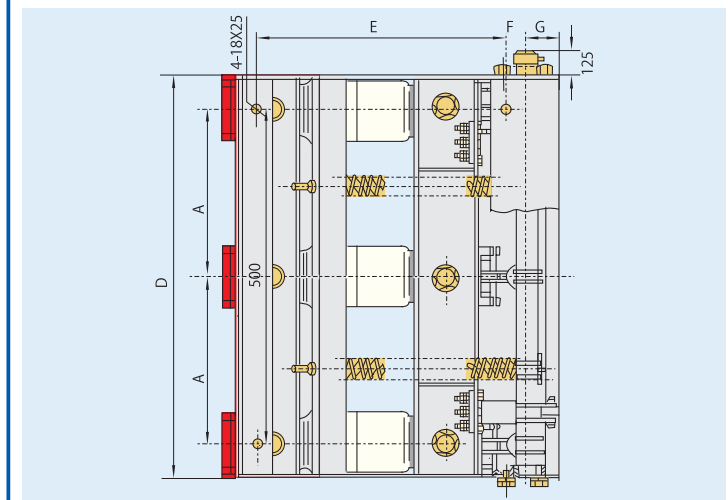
Внешний вид и монтажные размеры выключателя серии ZN28A-12
